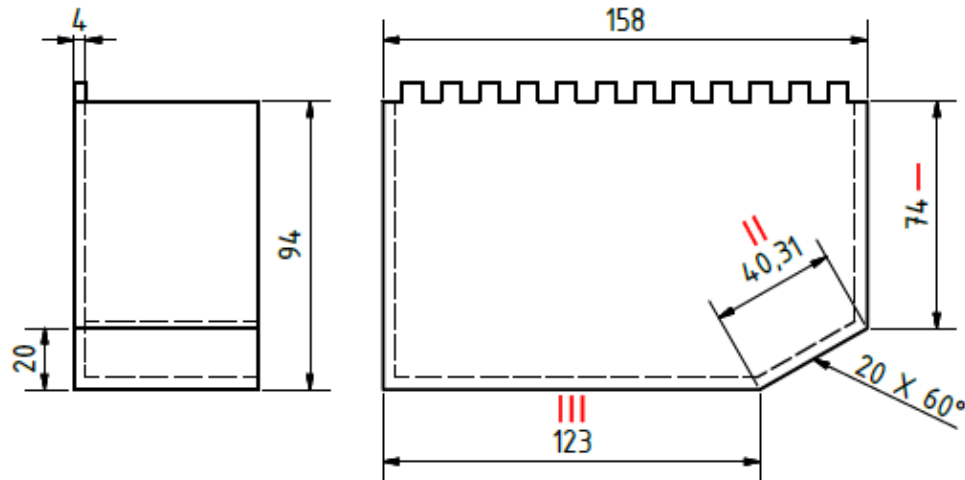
Tampa do Motor Parte I-Medidas em mm.
